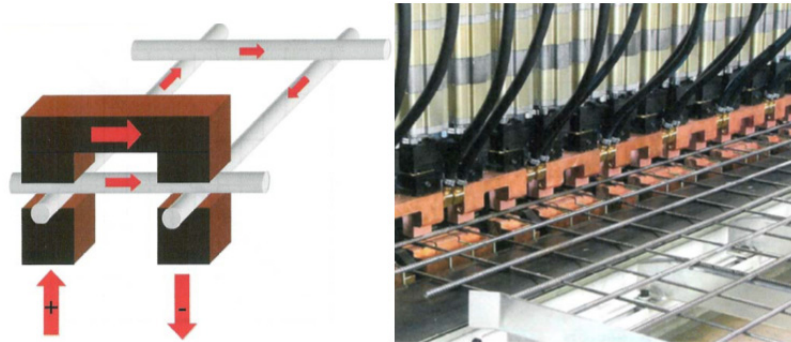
Exemplo de equipamento de soldadura indirecta por pontos múltiplos [16]
